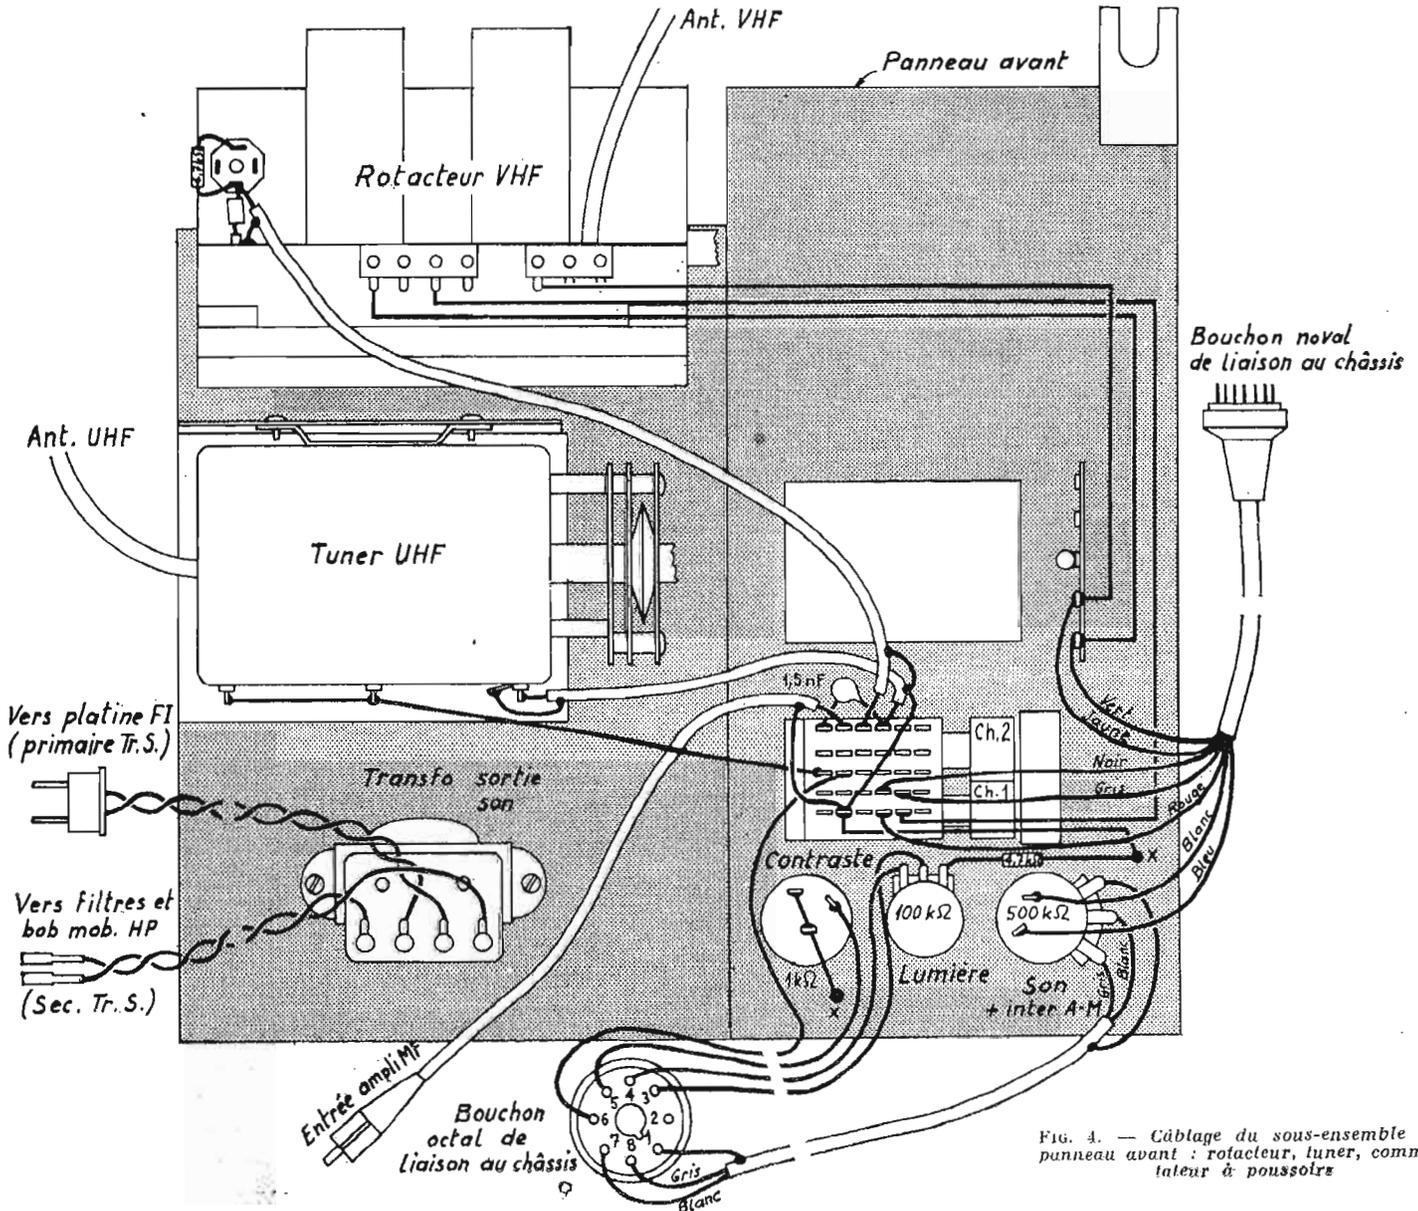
Câblage du sous-ensemble du panneau avant : rotacteur, tuner, commutateur à poussoirs
